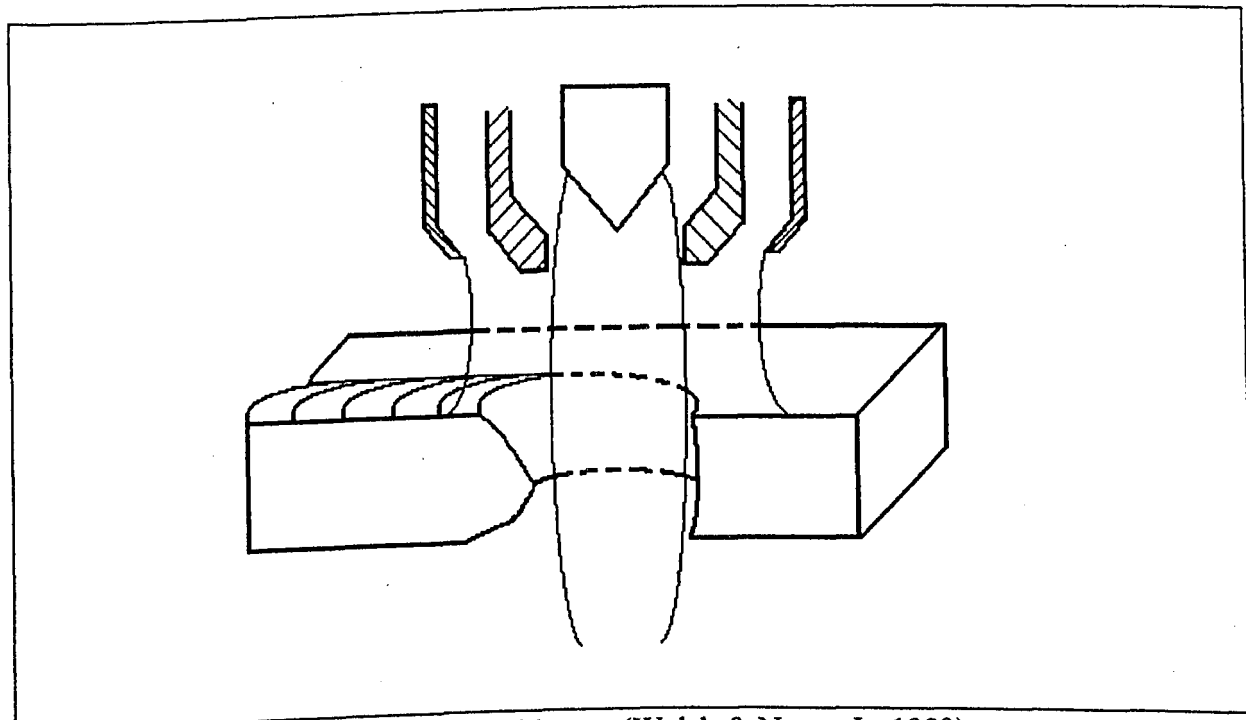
Técnica “keyhole” de soldagem (Walsh & Nunes Jr, 1989).
